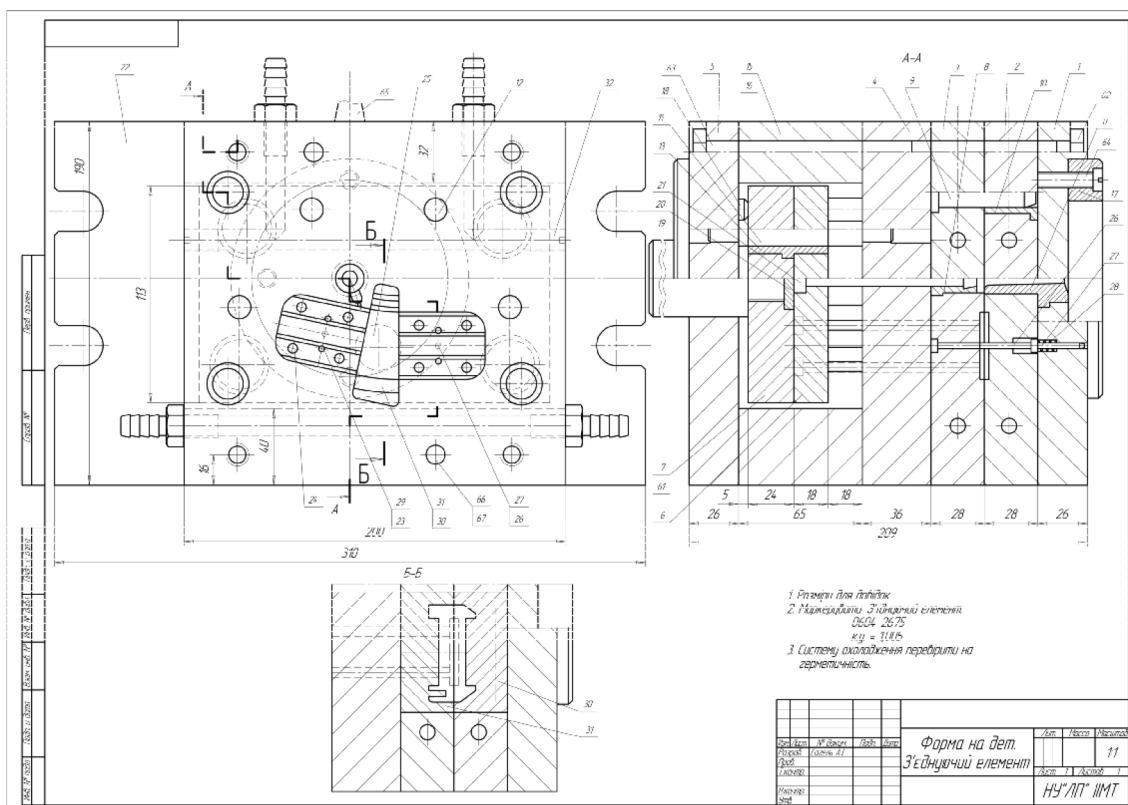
Кресленик пресформи для виготовлення кронштейну
